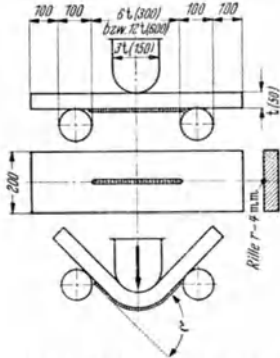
Nutschweißbiegeversuch (Schweißraupenbiegeprobe) nach O. KOMMERELL.
